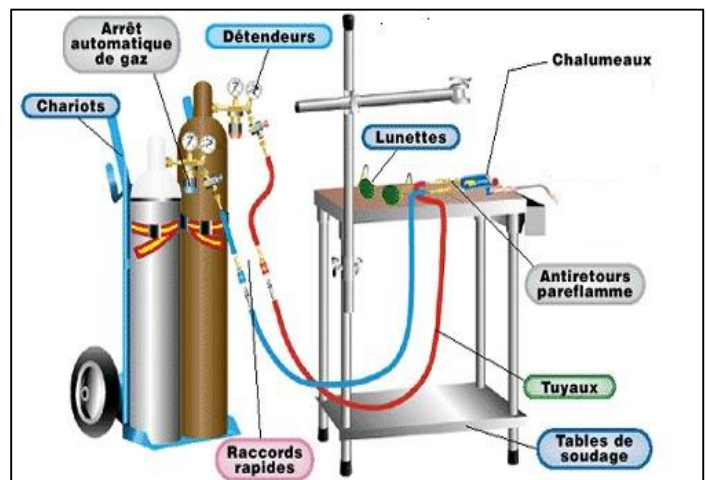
Soudage au gaz chalumeaux [13]
